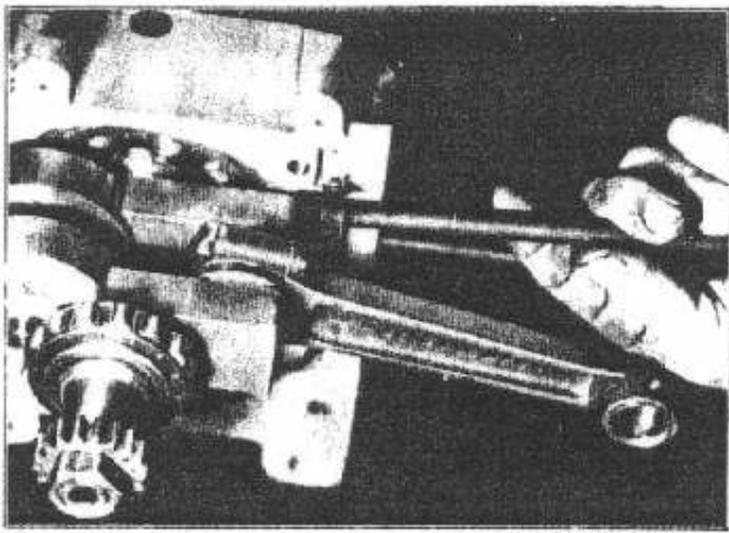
Prima di chiudere i due mezzi carter ricrebrare di piazzare il tirante per fissaggio testa e cilindro.
